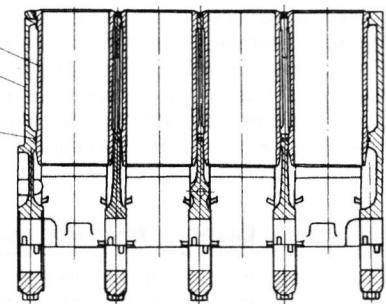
Установка гильз цилиндров: 1 – уплотнительное кольцо; 2 – блок цилиндров; 3 – гильза цилиндров
